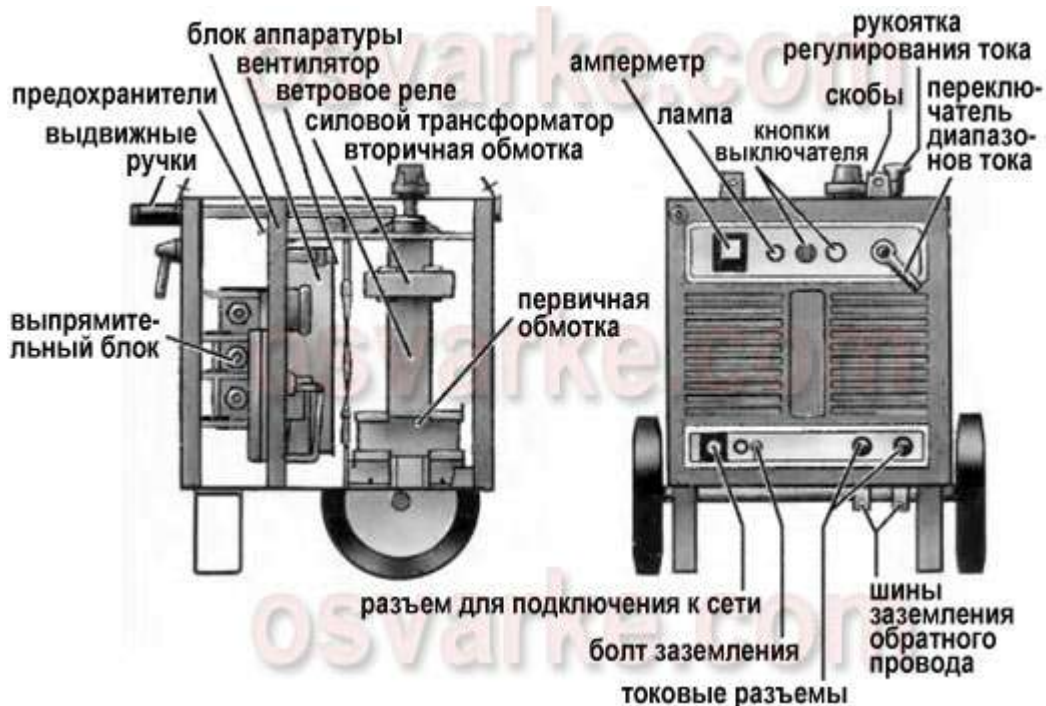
Устройство сварочного выпрямителя (с трансформатором с подвижными обмотками)
